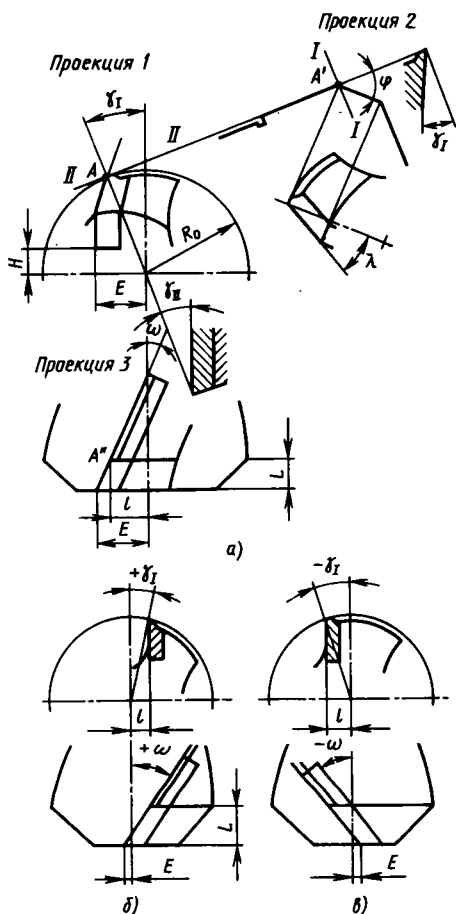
Параметры установки пластин или ножей у зенкеров, оснащенных пластинами из твердого сплава, и сборных зенкеров
